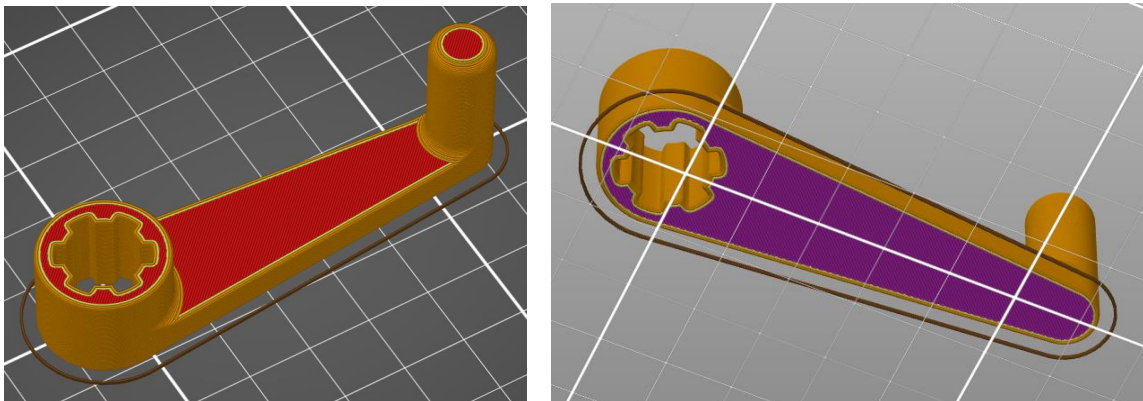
Vizualizace CAD formátu „.stl“ v programu „3D Print“ od společnosti Microsoft
